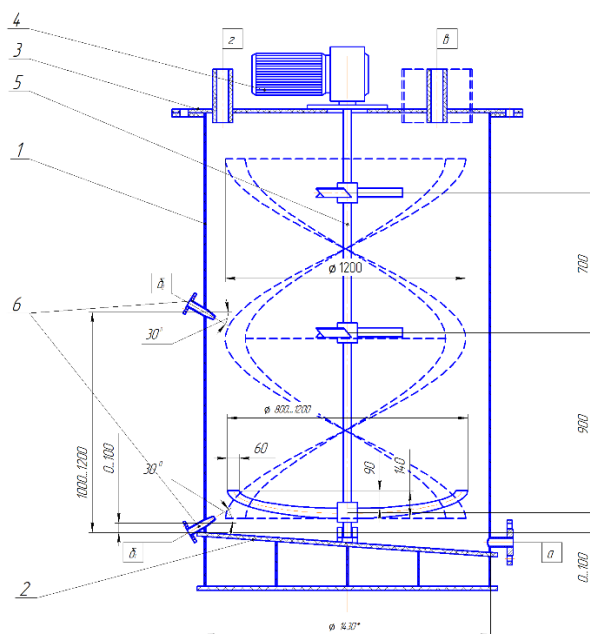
Аппарат конверсии. 1 – цилиндрическая обечайка корпуса; 2 – днище; 3 – крышка; 4 – привод механического перемешивающего устройства; 5 – механическое перемешивающее устройство; б – сопла; а – патрубок отвода суспензии и щелочного раствора; б<sub>1</sub>, б<sub>2</sub> – патрубки ввода суспензии и щелочного раствора от подогревателя ПС; в – патрубок ввода распульпованного осадка ЧСК; г – патрубок ввода щелочного раствора.
